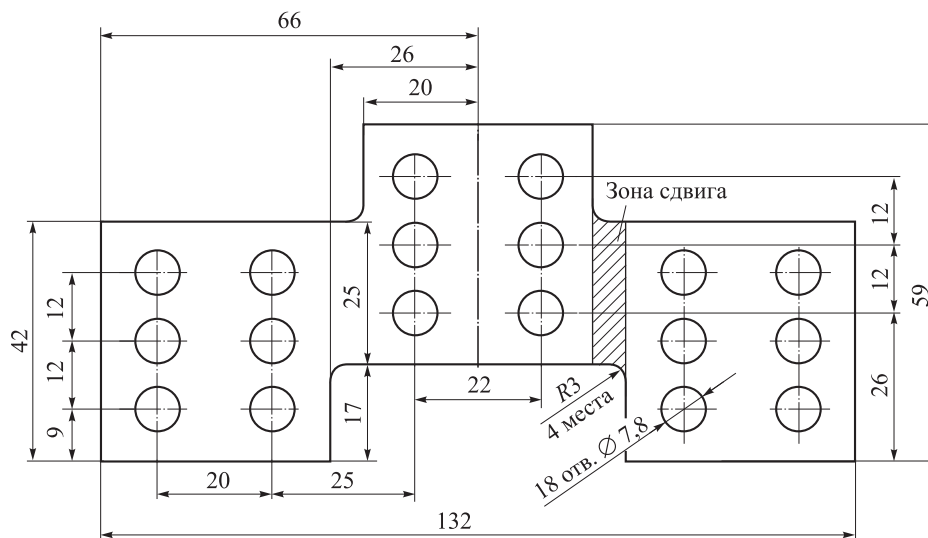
Предлагаемая форма образца для испытания на сдвиг
